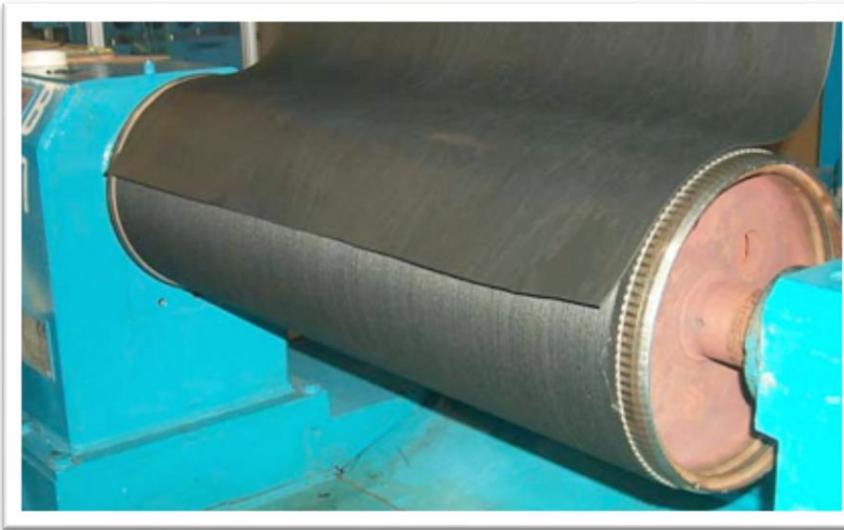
Colocación de la goma que va a ser enrollada sobre el molde
